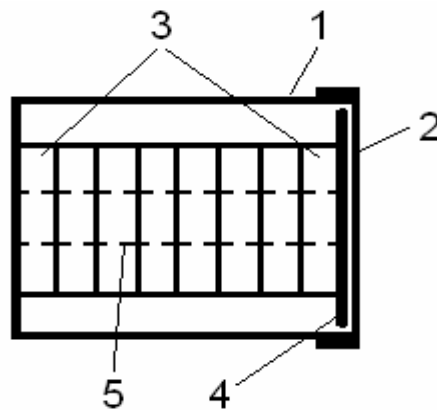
Конструктивная схема гидрофона: 1 – корпус, 2 – металлическая крышка, 3 – пьезокерамические кольца, 4 – мембрана, 5 – стержень.
